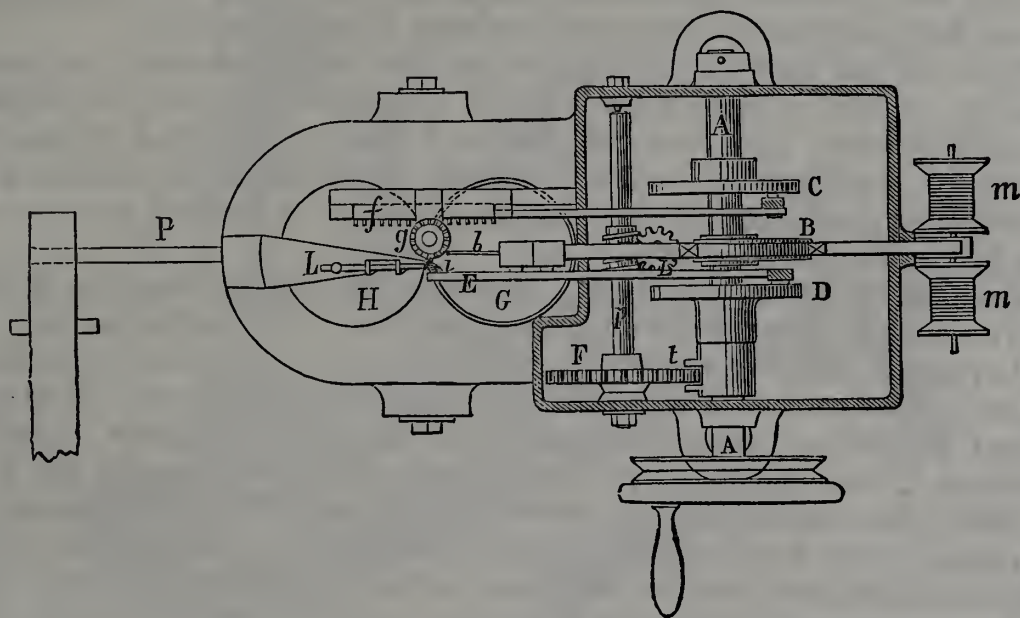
Machine à coudre les gants. Coupe horizontale.
